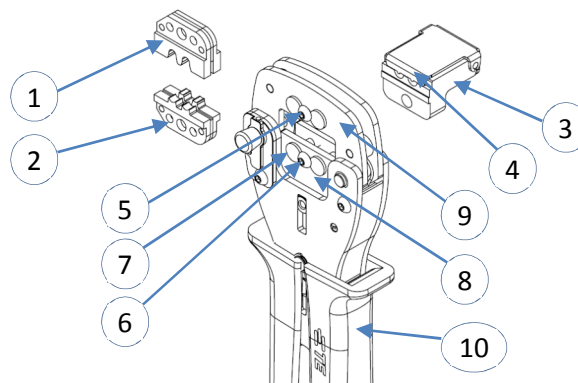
Explosionszeichnung des Handwerkzeugs inkl. Crimpmatrzensatz
